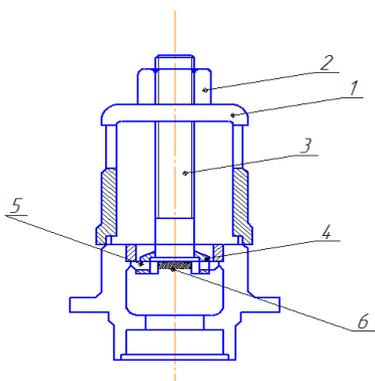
Съемник для выпрессовки обойм с помощью кулачков на пружинах
